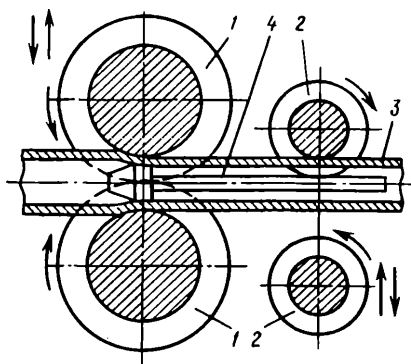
Схема прокатки трубы на автоматическом двухвалковом стане:
